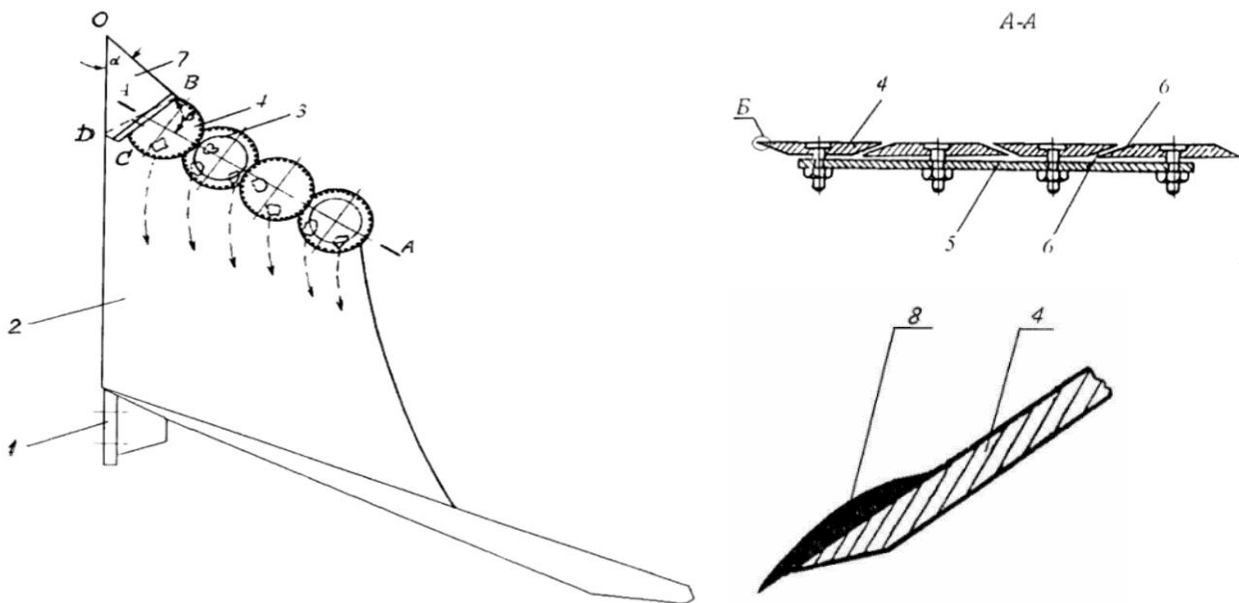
Корпус плуга з лемішем у вигляді дисків [106].
